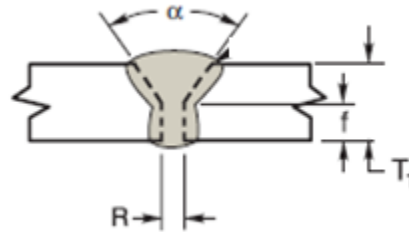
Sección de la soldadura SSW con tacón (Fuente: www.monografias.com)
